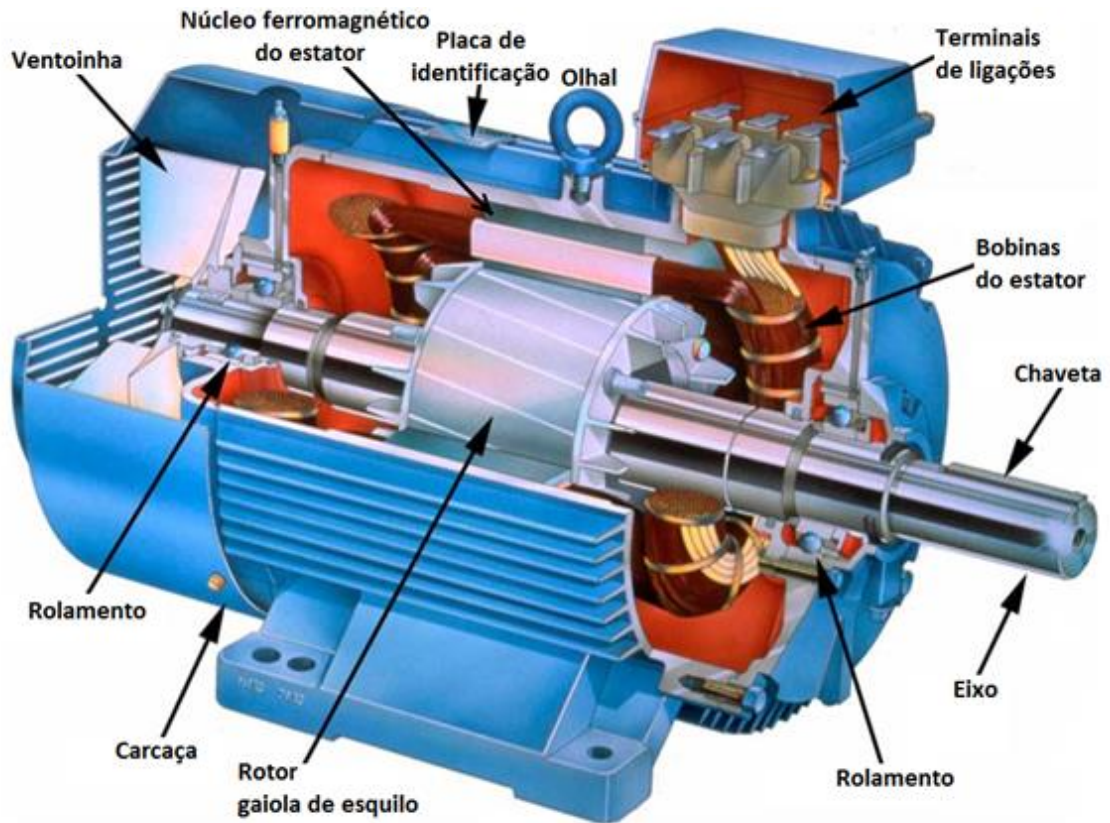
Vista em corte dos principais componentes de um MIT com rotor gaiola de esquilo.
